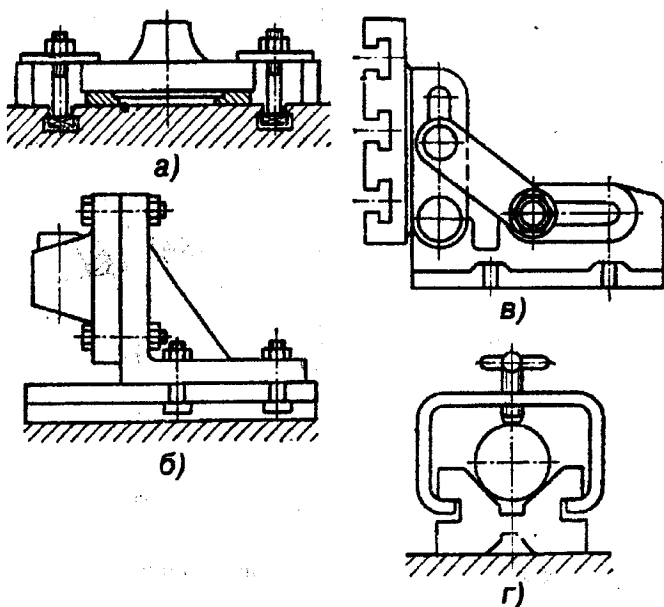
Пристосування для закріплення заготовок на свердильних верстатах
